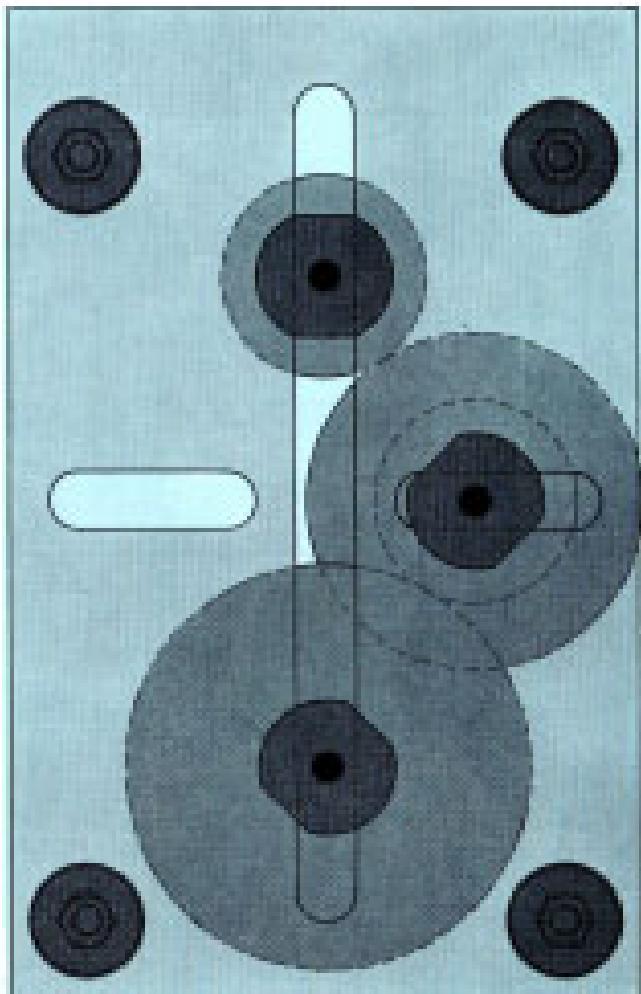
Die Handkurbel wird wie die Räder befestigt.
